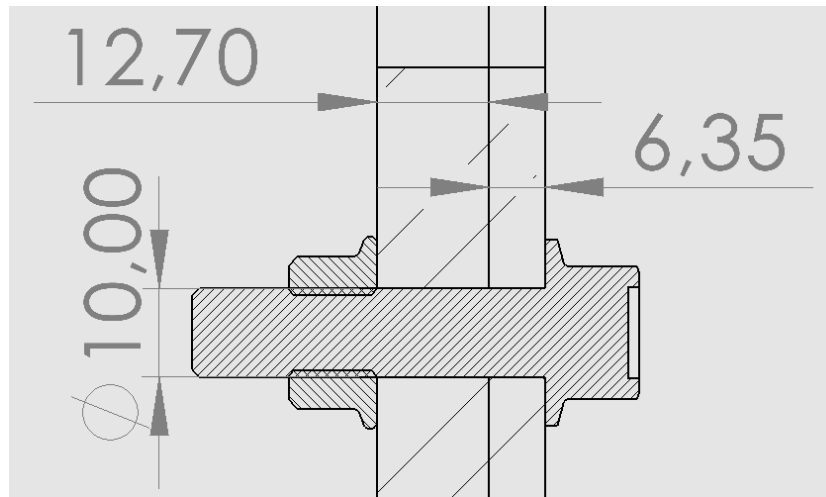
Dimensiones de la empaquetadura y el bulón del enganche.
